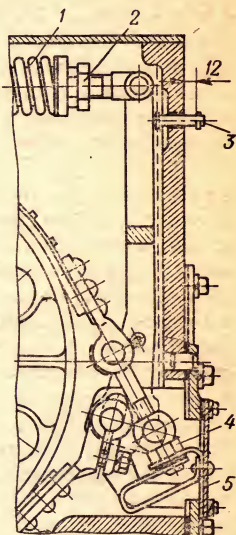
Регулировка тормоза солнечной шестерни трактора Т-4А:
